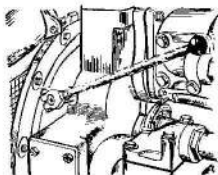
Рычаг отключения двигателя трактора и неработающего двигателя.
